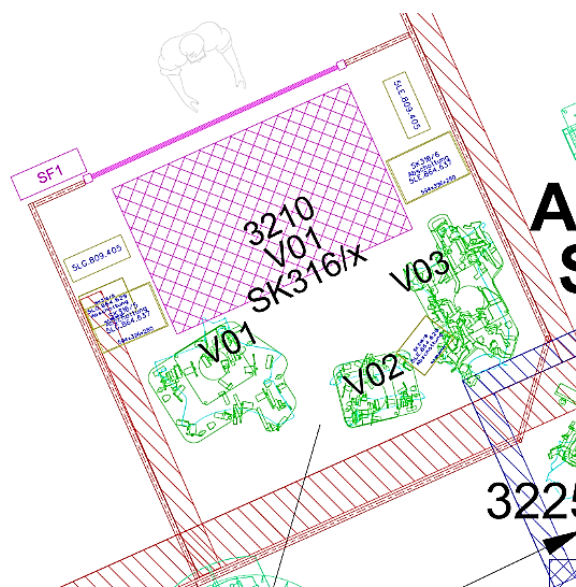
Layout základacího pracoviště ST3210 varianty 2
